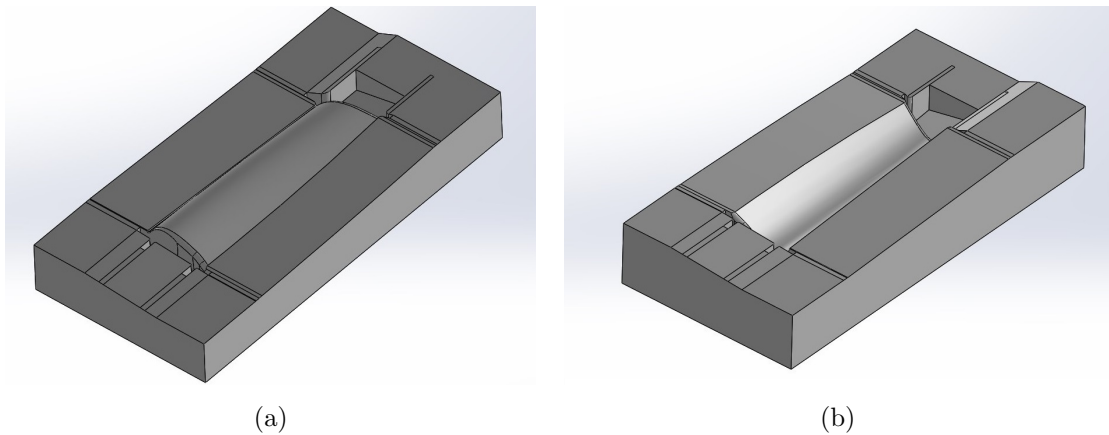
(a) Meio molde inferior do molde, (b) Meio molde superior do molde
